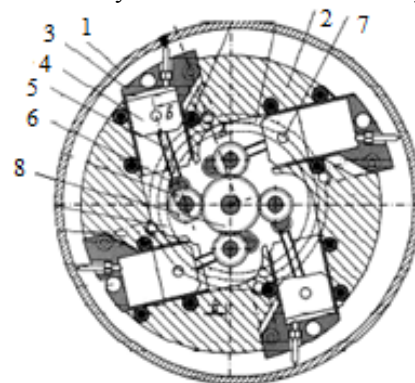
Конструктивна схема роторно-поршневого двигуна внутрішнього згоряння [1]: 1 – корпус; 2 – блок циліндрів; 3 – плаваючий циліндр; 4 – поршень; 5 – шатун; 6 – кривошип; 7 – поршневий палець; 8 – блок шестерень
